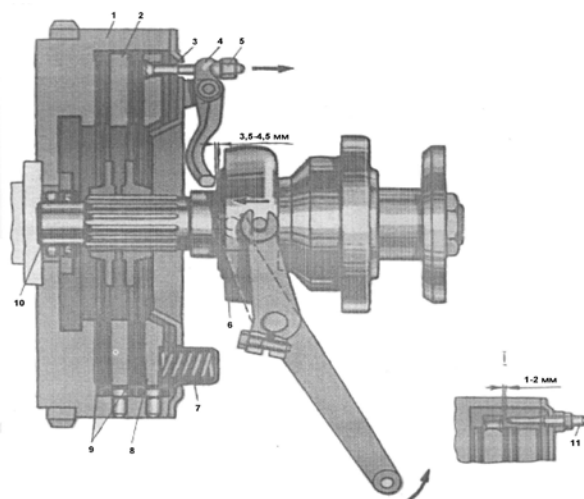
Муфта сцепления: 1-регулировка отхода среднего ведущего диска; 2-маховик двигателя; 3-болт; 4-рычаг отжимной; 5-гайка регулировочная; 6-выжимной подшипник; 7-пружина; 8-диск ведущий; 9-диск ведомый; 10-выходной вал; 11-регулировочной болт.
